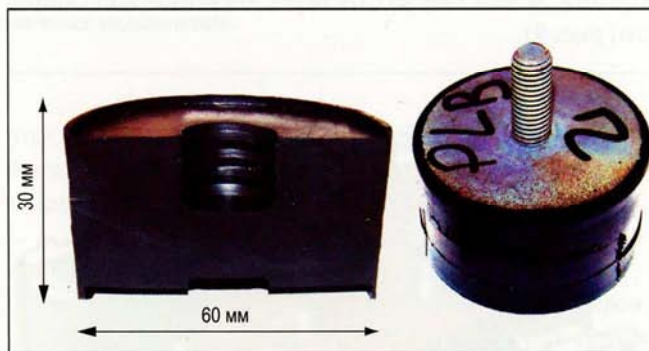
Резиновая опора, изготовленная литьем под давлением с применением системы TurboCure
